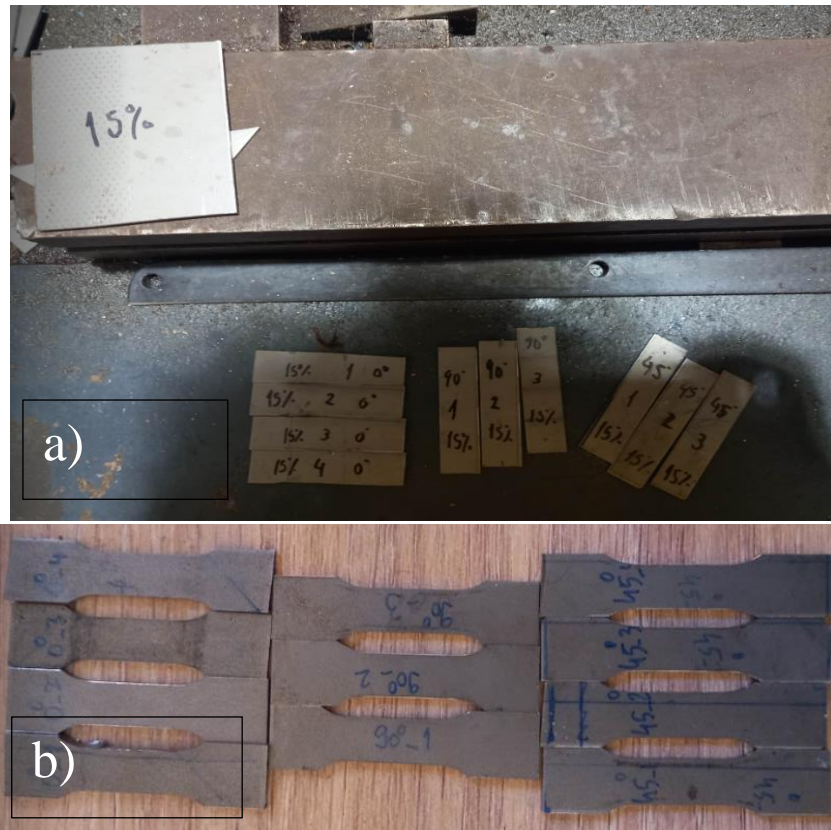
a) Provetes depois de serem cortados na guilhotina; b) Provetes após maquinagem
